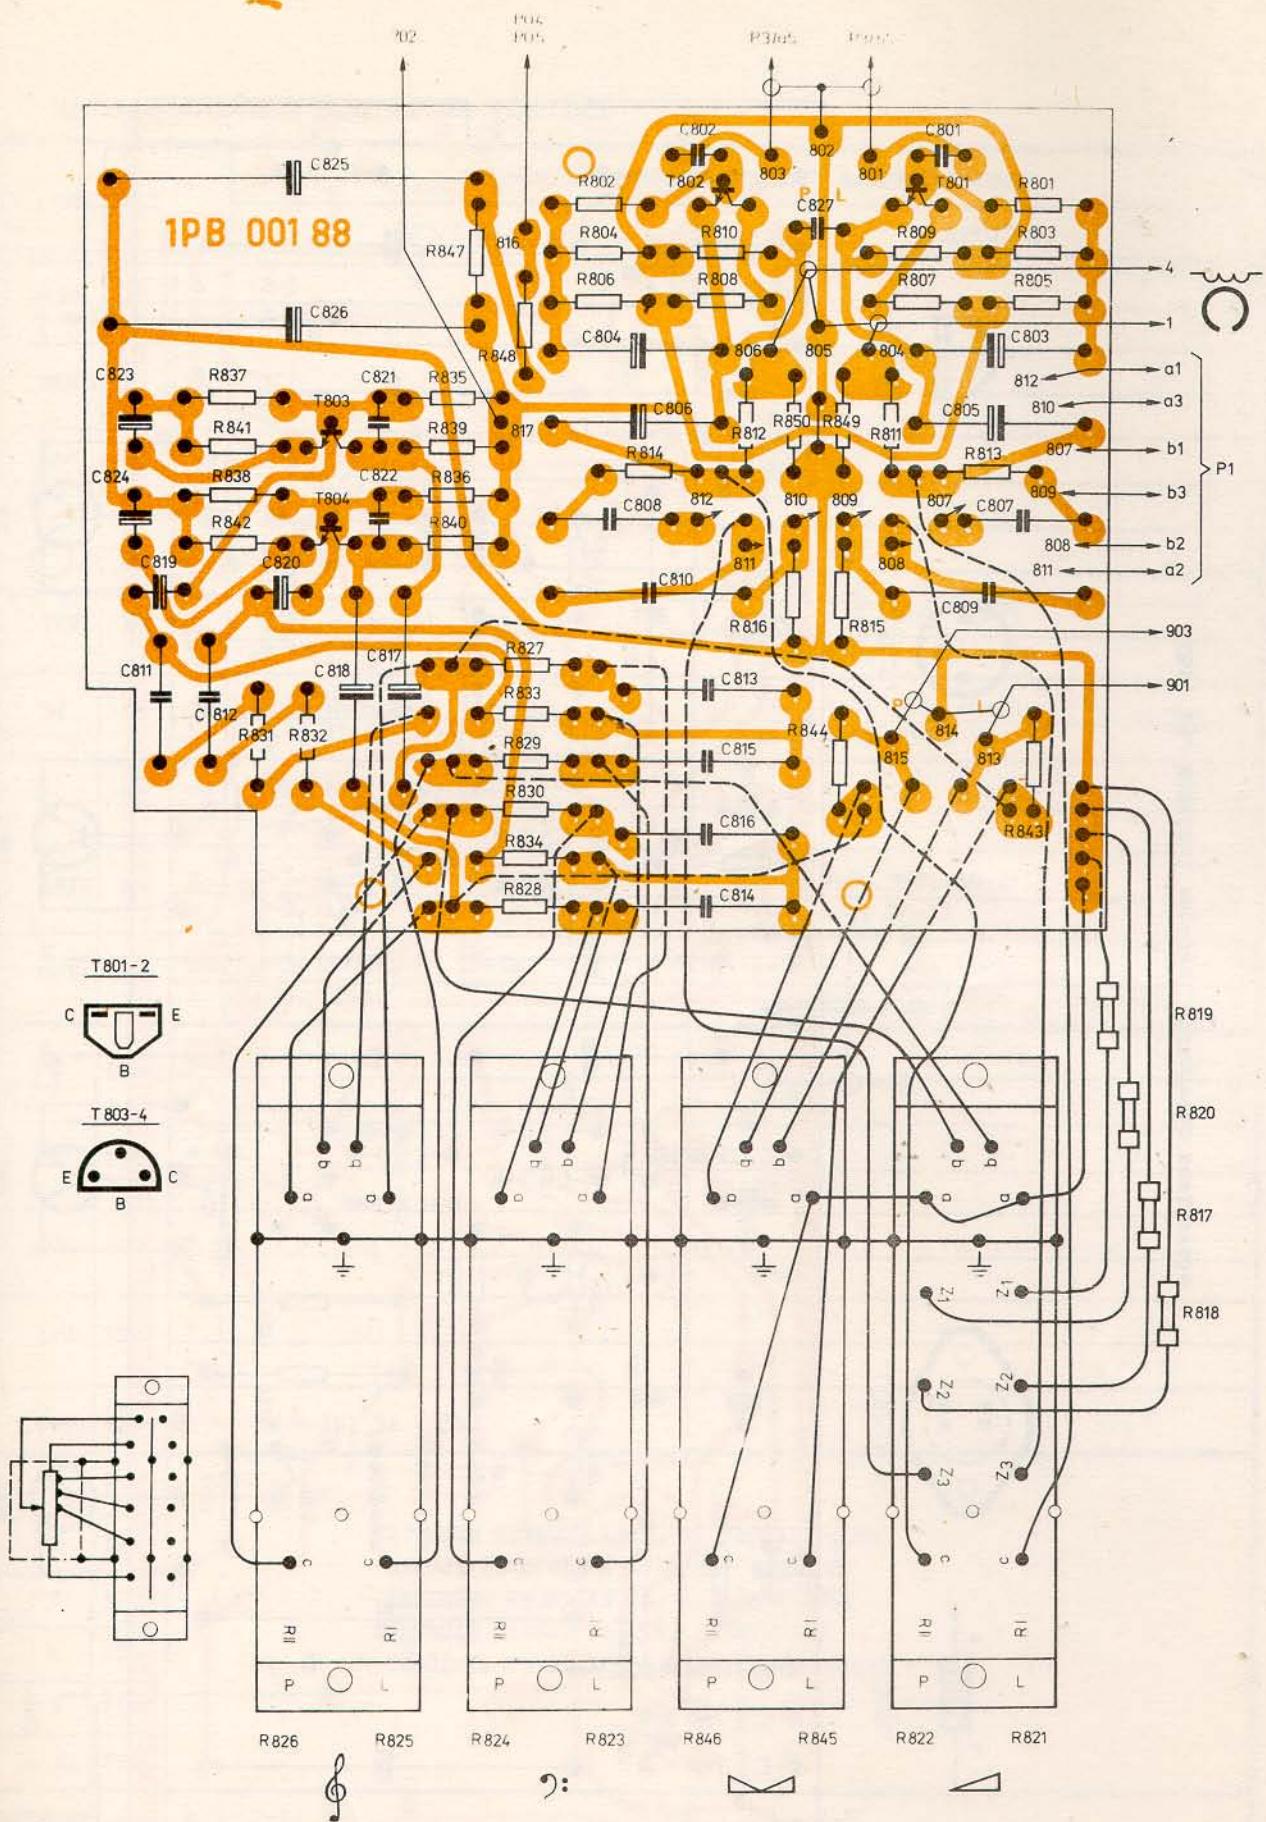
Montážní zapojení korekčního předzesilovače pro přenosku
